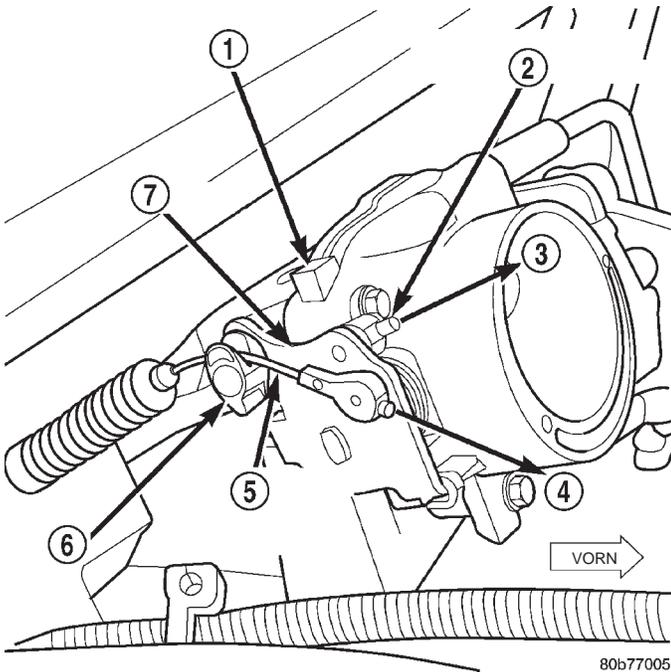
Gaszug am Kugelgelenk—4.7L-V8-Motor
